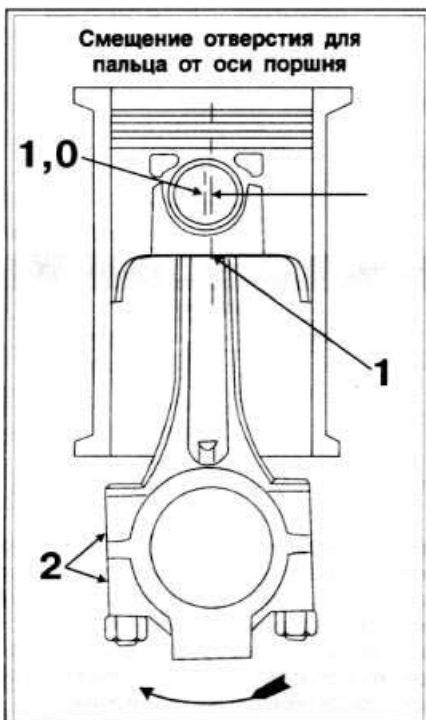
Схема установки и положение деталей шатунно-поршневой группы на двигателе:
